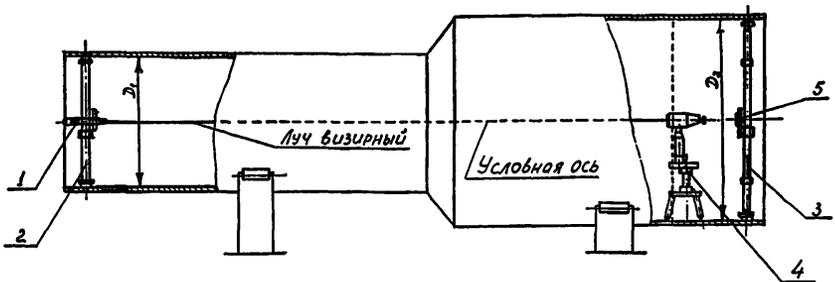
Схема контроля круглости и прямолинейности корпуса цилиндрического аппарата
